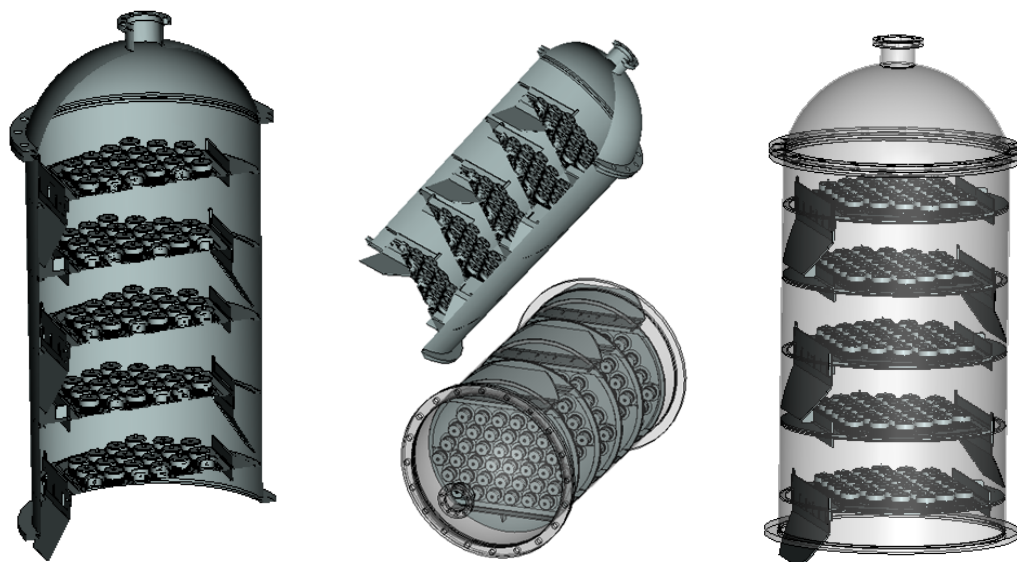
Трехмерная сборка верхней части колонны с плоскостью обрезки и прозрачным корпусом
